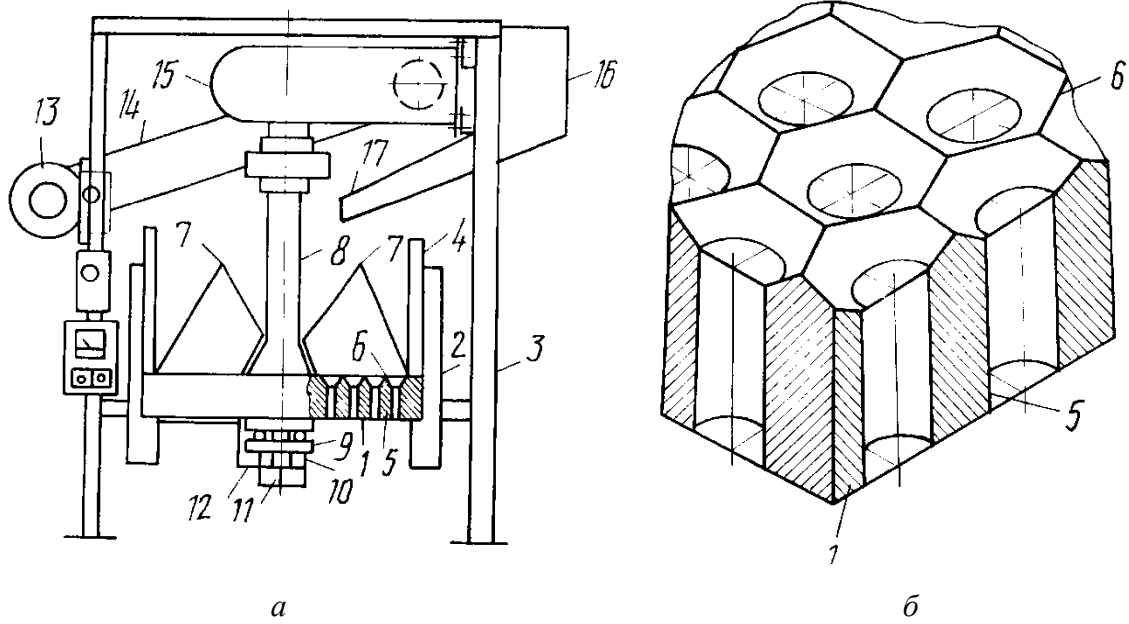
Пресс-гранулятор: 1 – матрица; 2 – обойма; 3 – рама; 4 – кольцо; 5 – прямые режущие кромки; 6 – ячейки; 7 – конические вальцы; 8 – приводной вал; 9 – упорный подшипник; 10, 12 – гайка; 11 – подрезной нож; 13 – электродвигатель; 14 – клинременная передача; 15 – редуктор; 16 – бункер; 17 – задвижка
